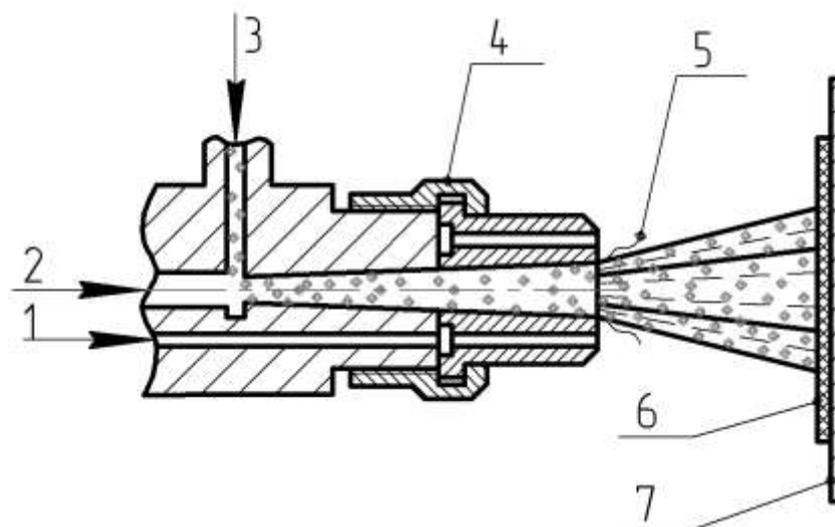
Схема газопламенного напыления: 1 – кислород и горючий газ; 2 – транспортирующий газ; 3 – напыляемый порошок; 4 – сопло; 5 – факел газового пламени; 6 – напыленное покрытие; 7 – напыляемая поверхность
